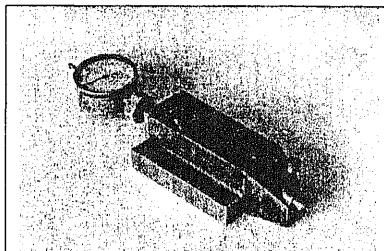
Пружинная оправка для алмазного выглаживания цилиндрических и торцовых поверхностей
